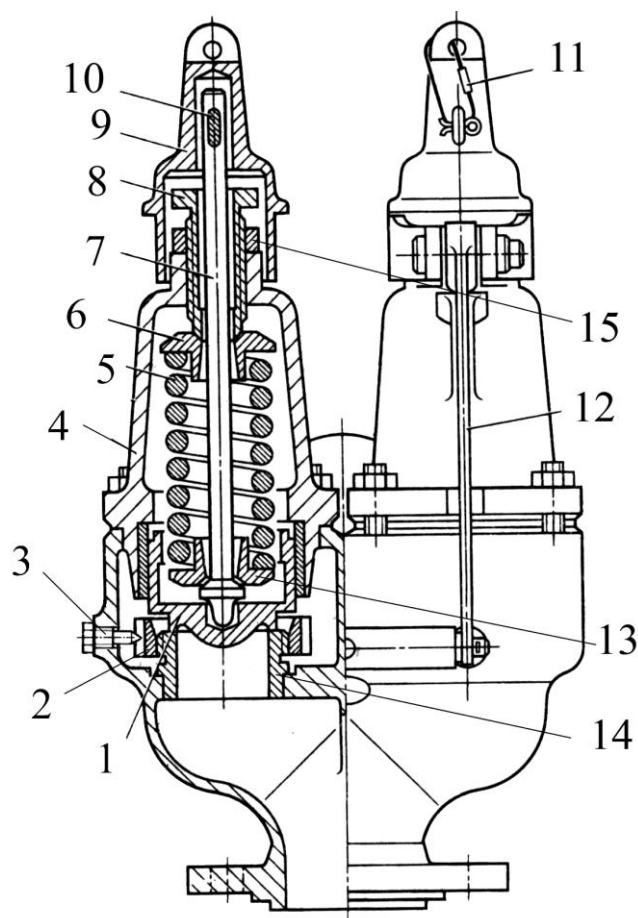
Сдвоенный предохранительный клапан:
